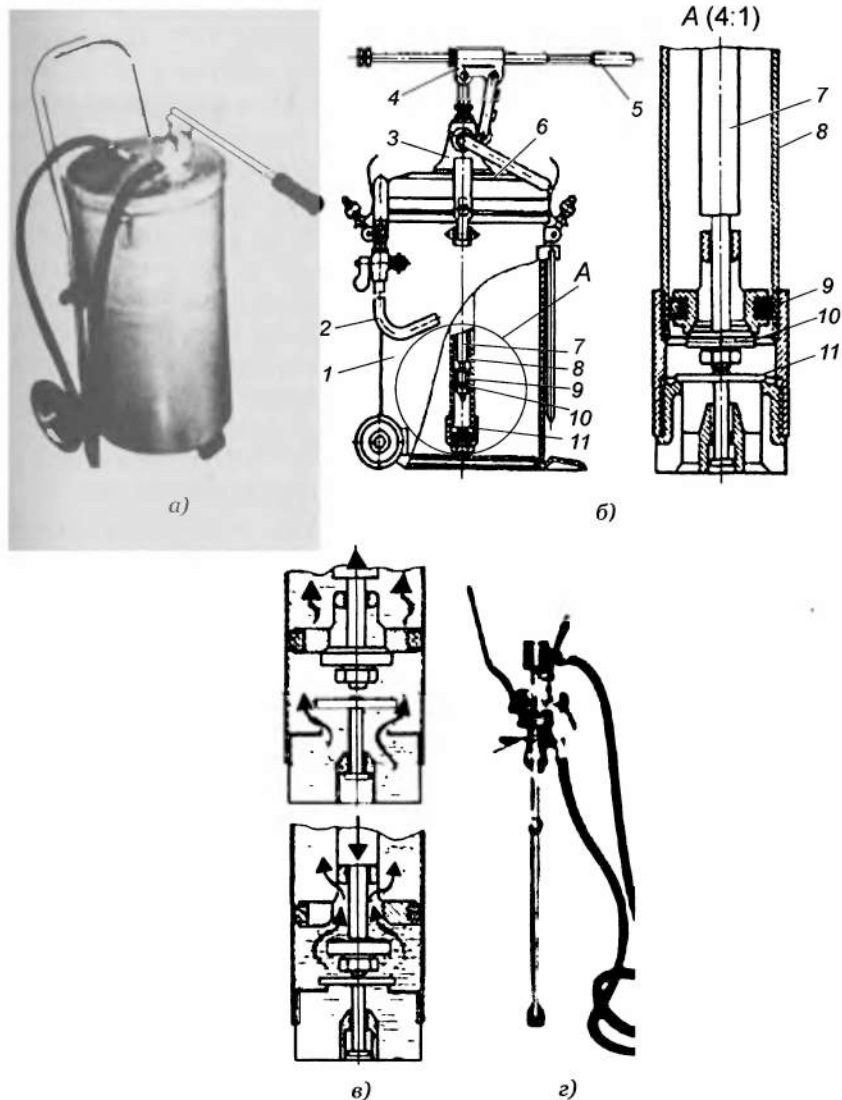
Передвижной маслораздатчик (а–в) и ручной насос (г) переносного маслораздатчика для заправки автомобиля: а — внешний вид; б — устройство; в — работа; 1 — резервуар (бочка); 2 — раздаточный наконечник; 3 — корпус насоса; 4 — рычажный механизм; 5 — рукоятка; 6 — крышка бака; 7 — шток; 8 — цилиндр насоса; 9 — поршень; 10 — перепускной клапан; 11 — всасывающий клапан
